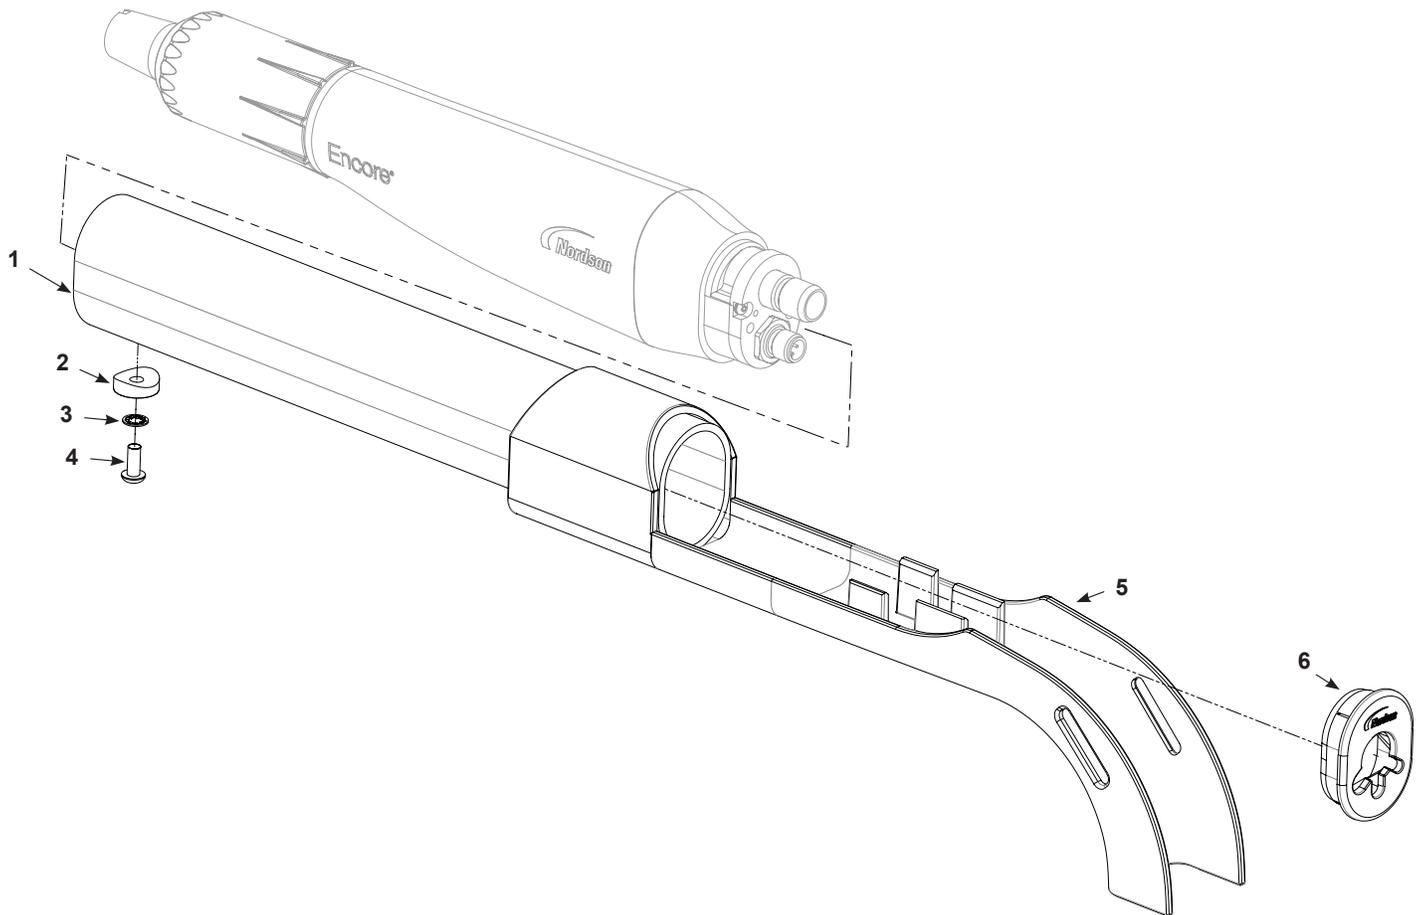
Pezzi della pistola a spruzzo con montaggio su tubo
